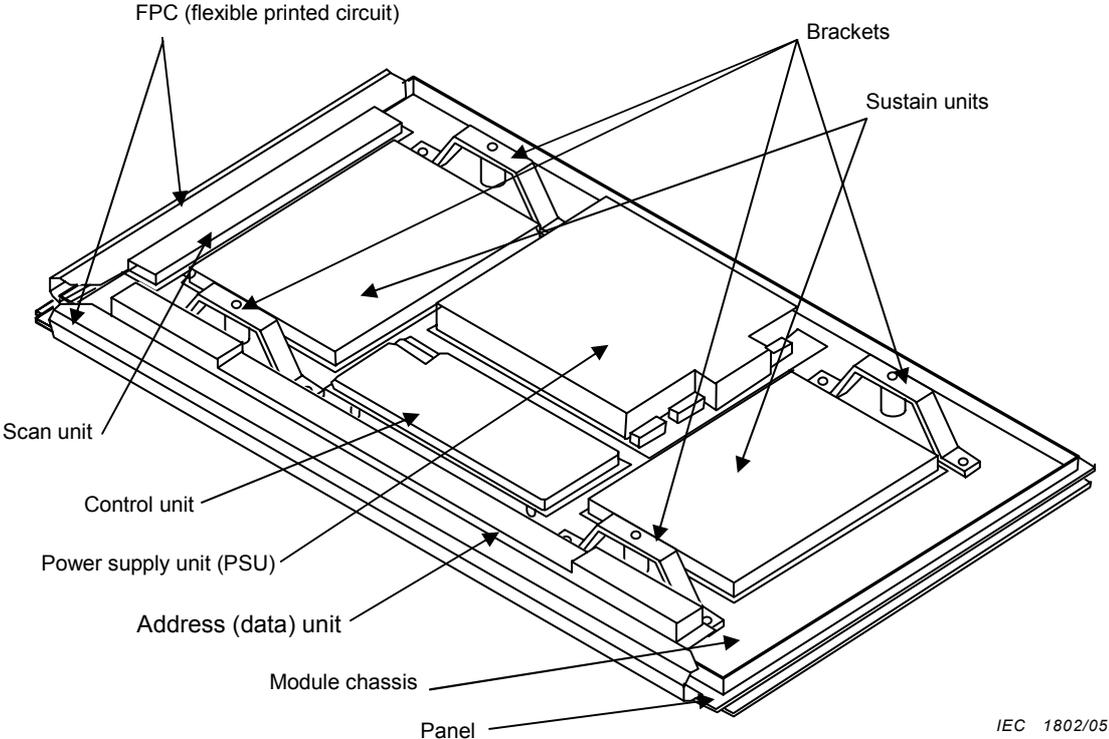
Vue d'ensemble d'un exemple de module PDP
